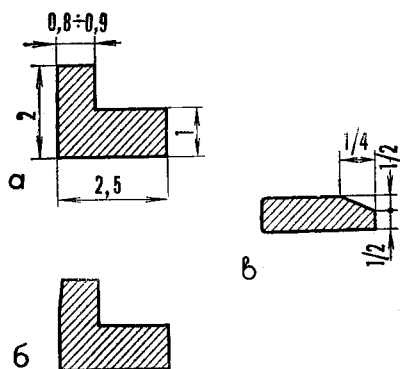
Поршневые кольца: а — L-образные; б — форма кольца после притирки; в — переделка обычного кольца
